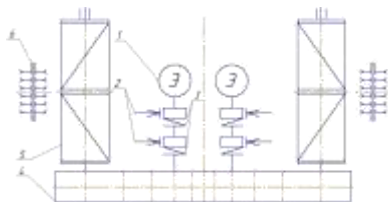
Конструкция с планетарным шестеренчатым редуктором (схема №6)
